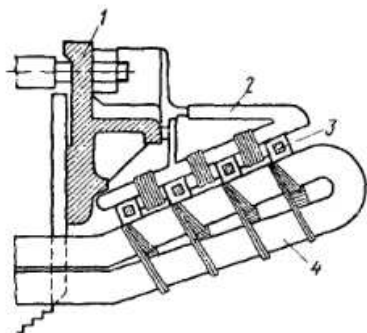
Крепление лобовых частей обмотки статора турбогенератора
